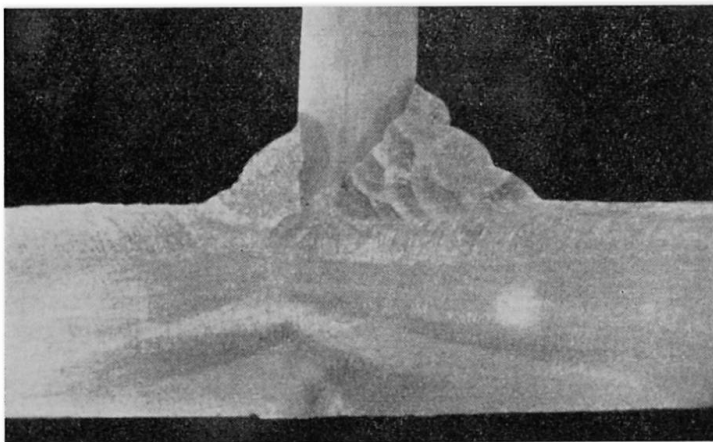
Einzelheit zu Fig. 8. Makroschliff einer CO₂-Untergurt-Schweißung.
